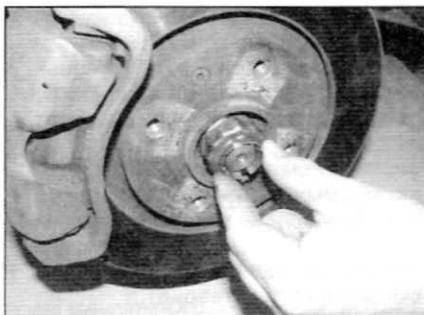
, б. ...и снимите стопорный колпачок с гайки крепления полуоси
